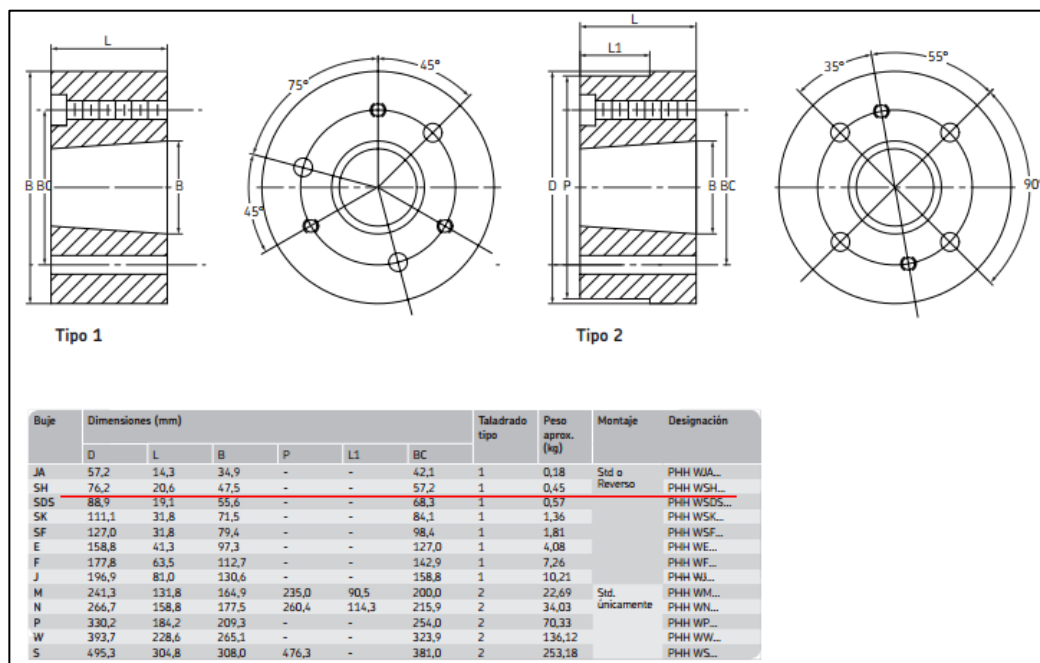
Tabla de dimensiones de masa soldable (Catálogo SKF)
